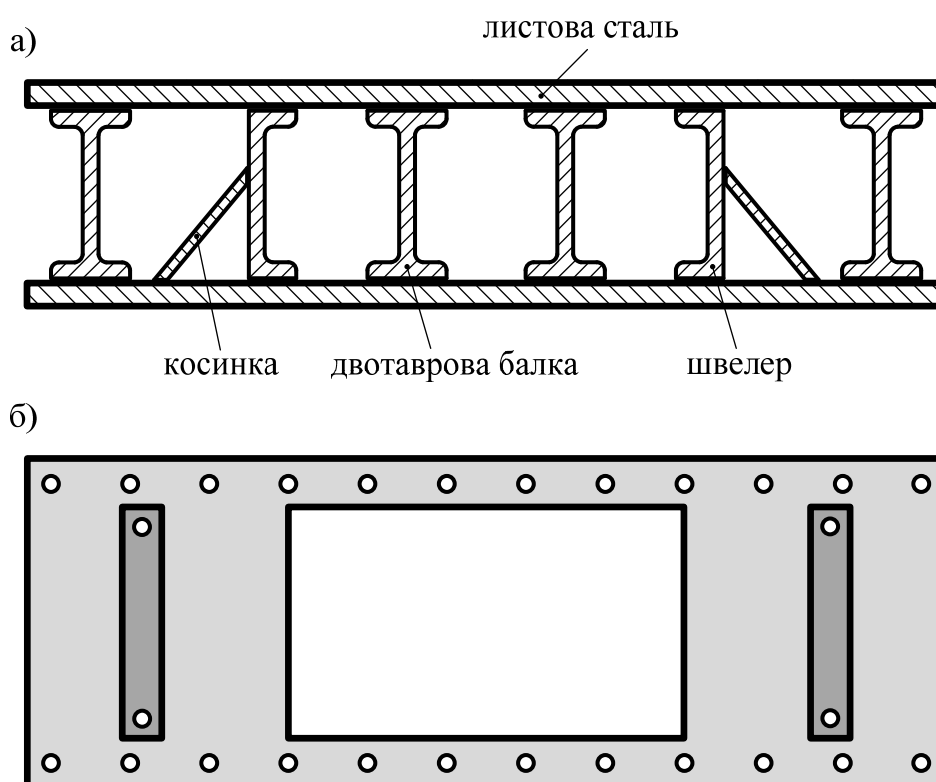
Фундаментна плита: розріз (а); вигляд зверху (б)
